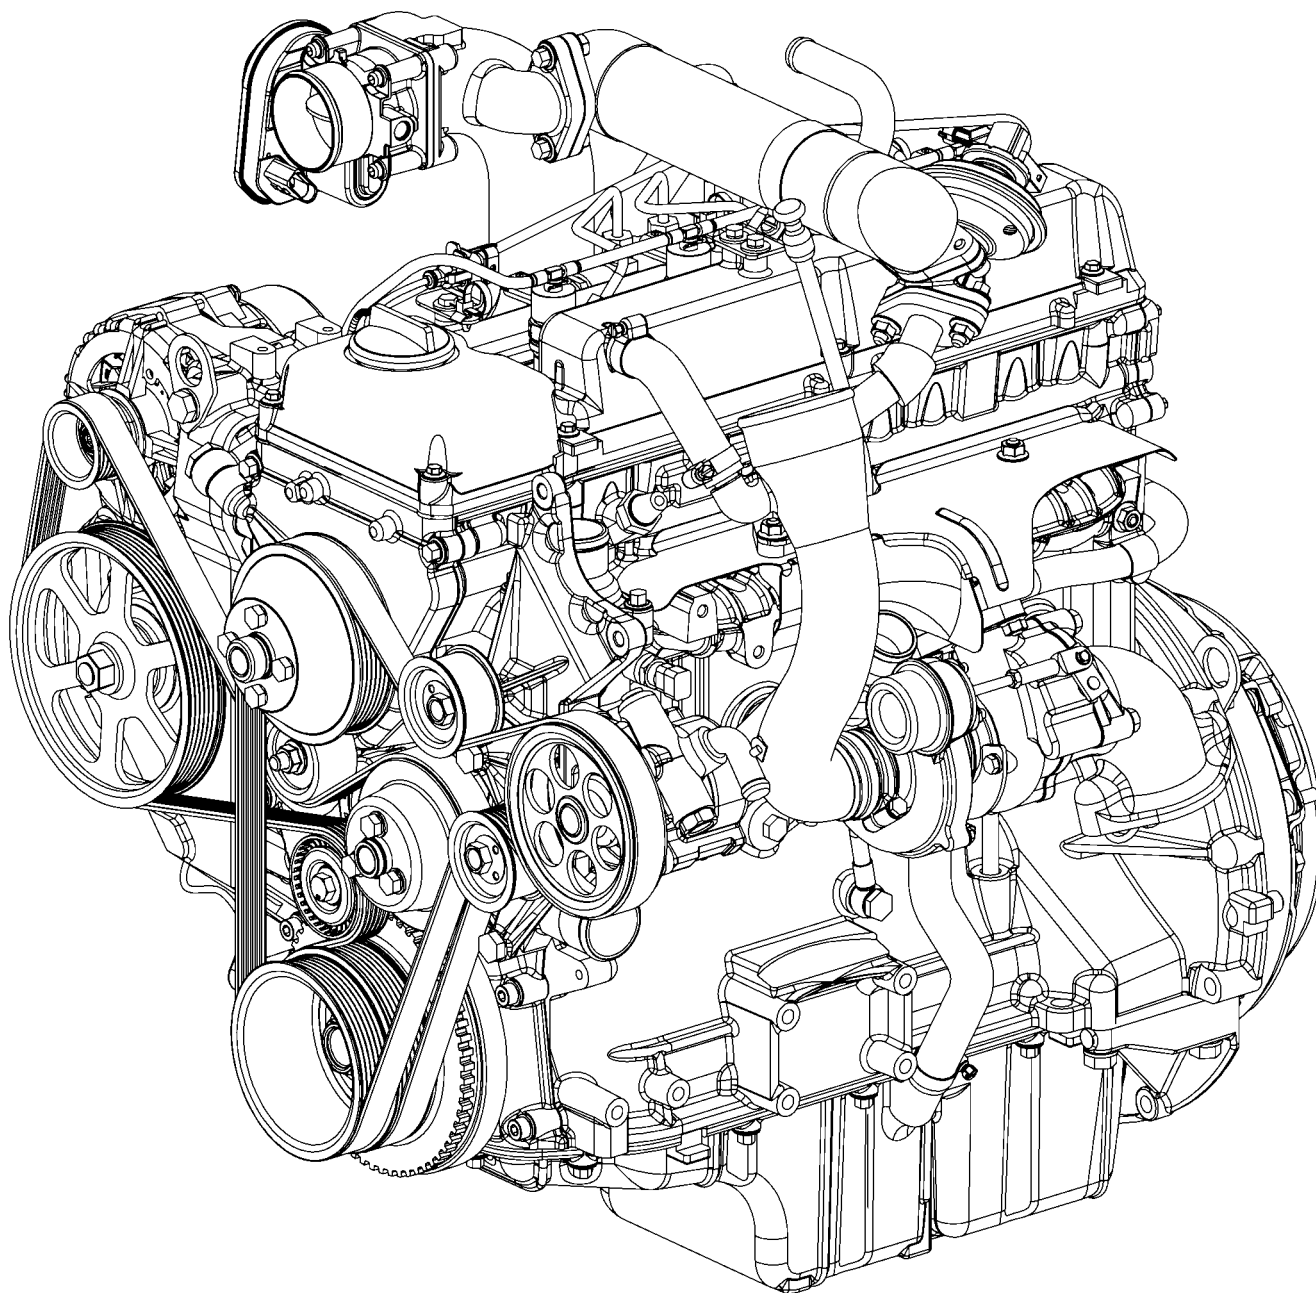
Общий вид двигателя для автомобилей, изготавливаемых на платформе УАЗ-3163 «Патриот», в комплектации без компрессора кондиционера с генератором 80А или 90А.
